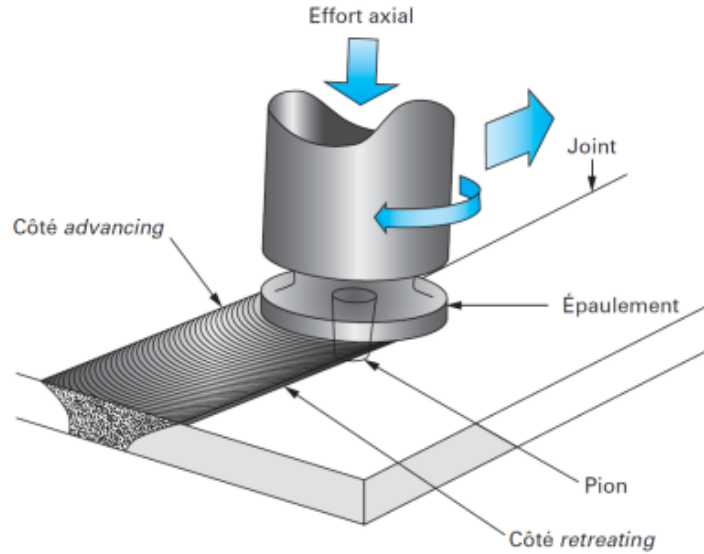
Le principe du procédé du soudage FSW. [26]
